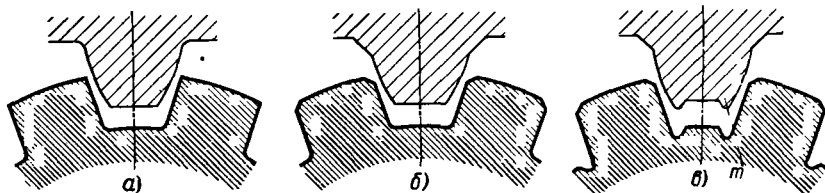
Профили режущего зуба червячной фрезы при обработке шлицев:
